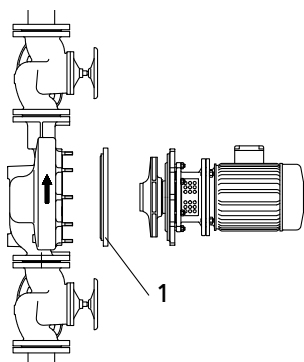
Horizontaler Einbau mit Blindflansch (1 = Blindflansch, Zubehör)
